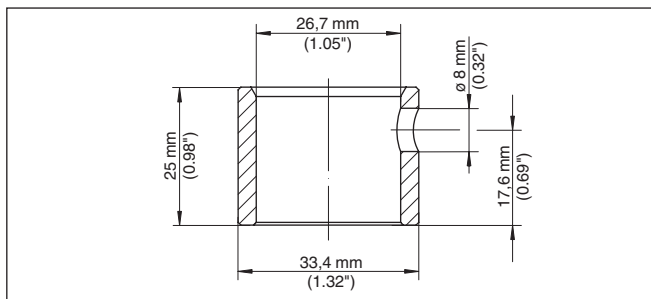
Dimensioni tronchetto a saldare PMC 1" - VEGABAR 82
